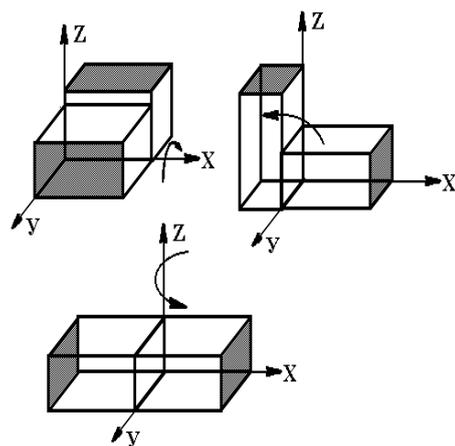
,б. Поворот заготовки вокруг координатных осей.
